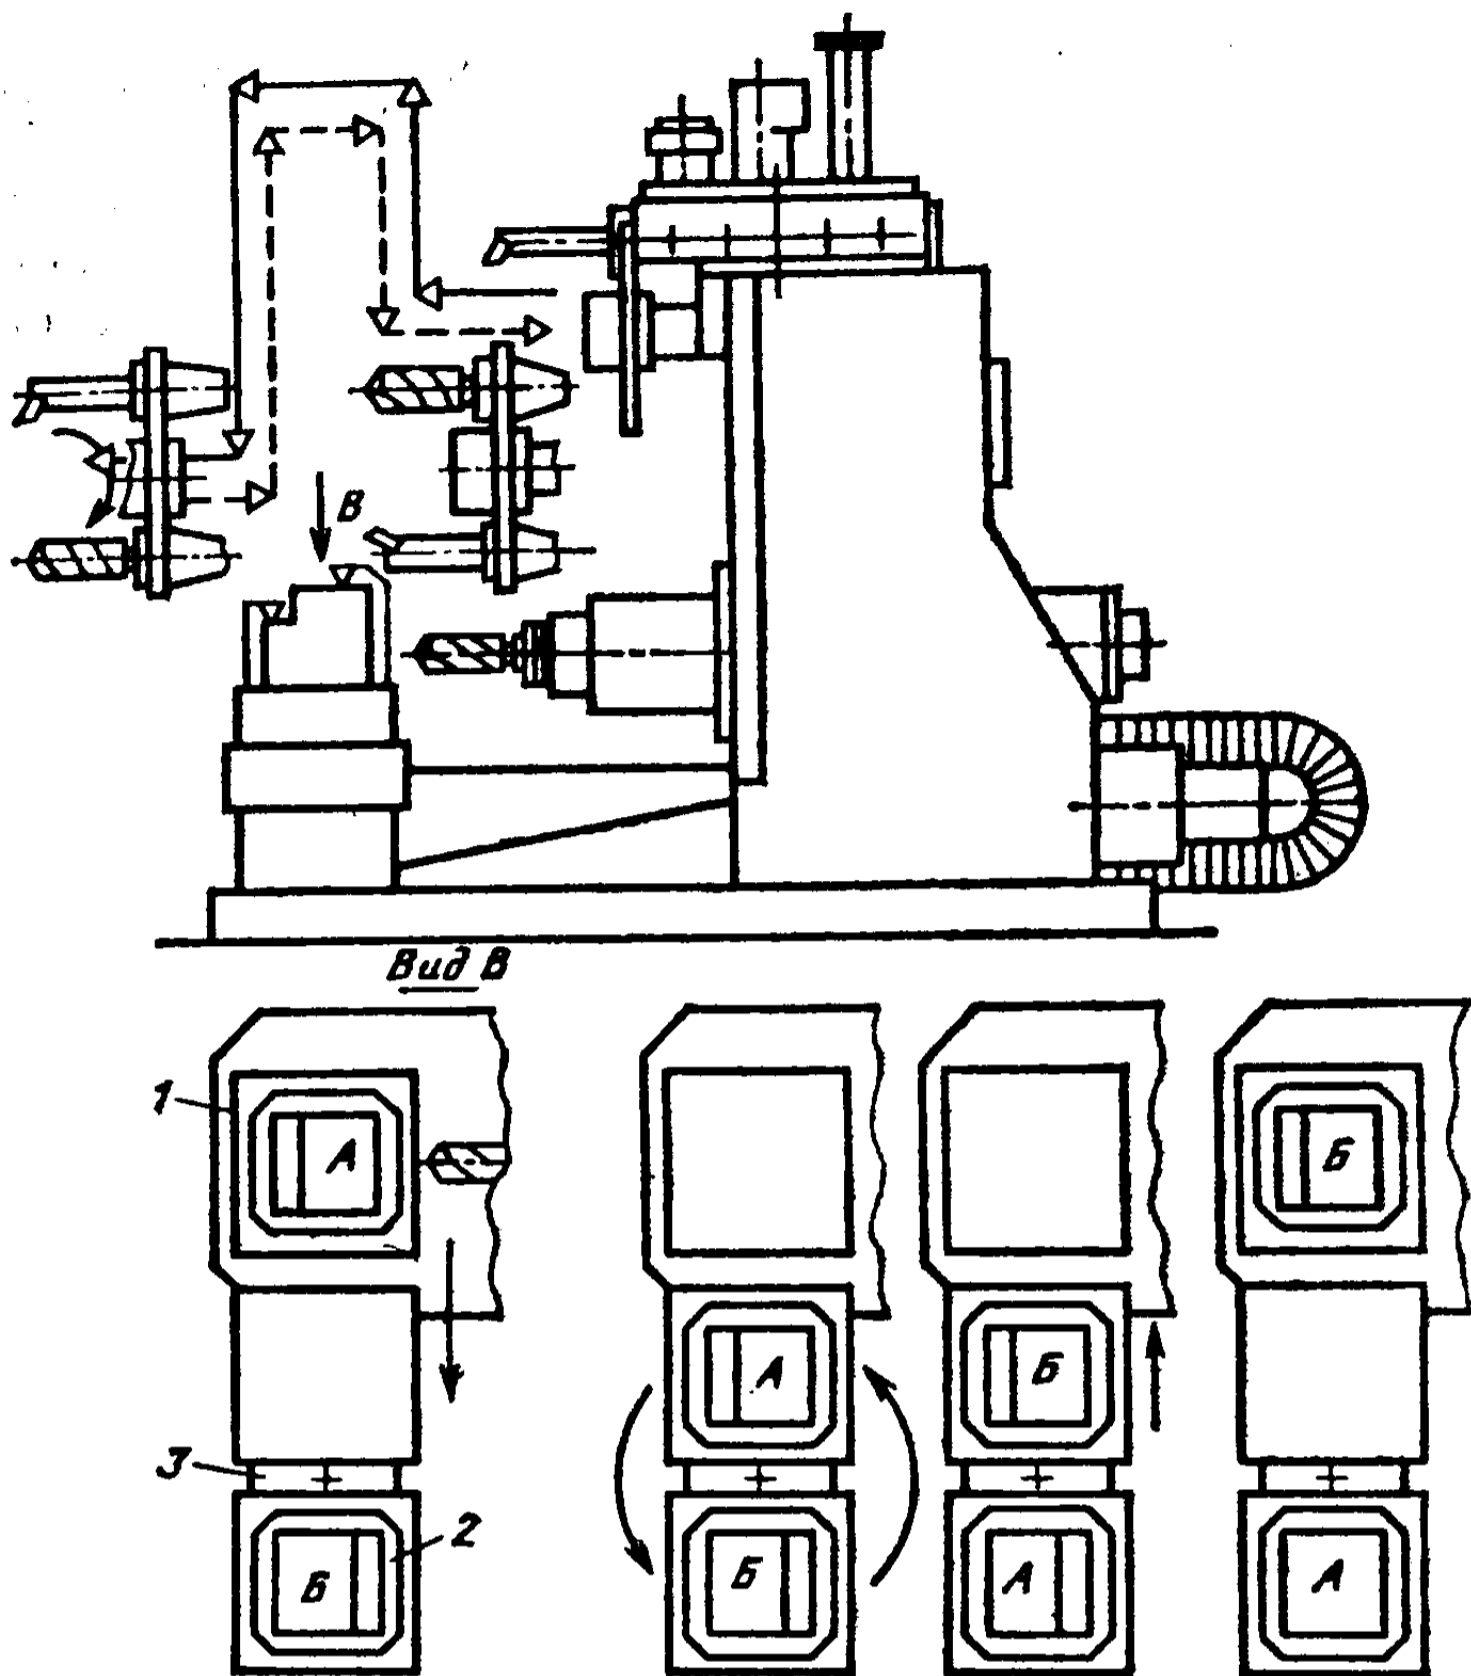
Многоцелевой станок с автоматической сменой заготовки и инструмента
